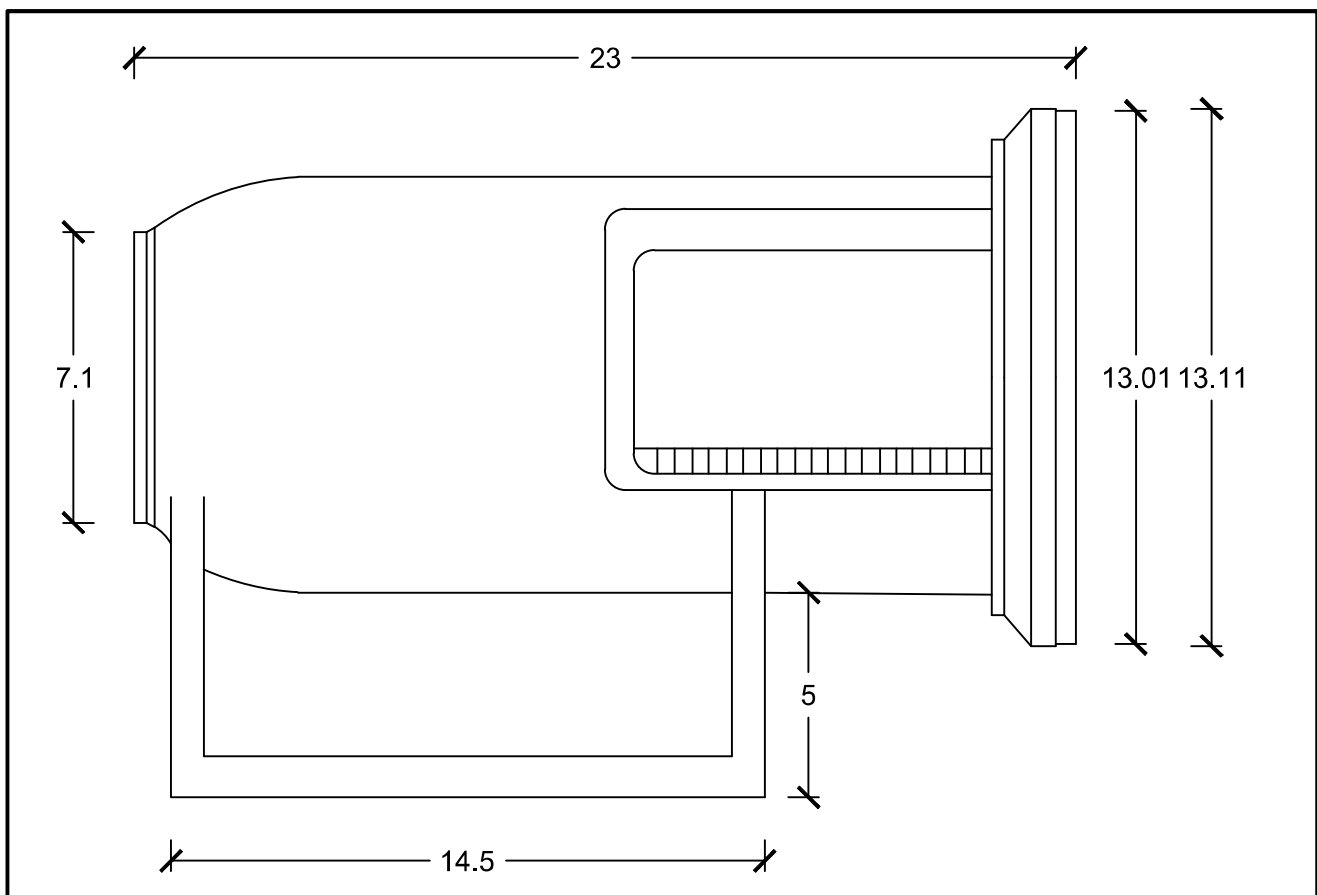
Vista frontal anterior del cuerpo de la turbina
